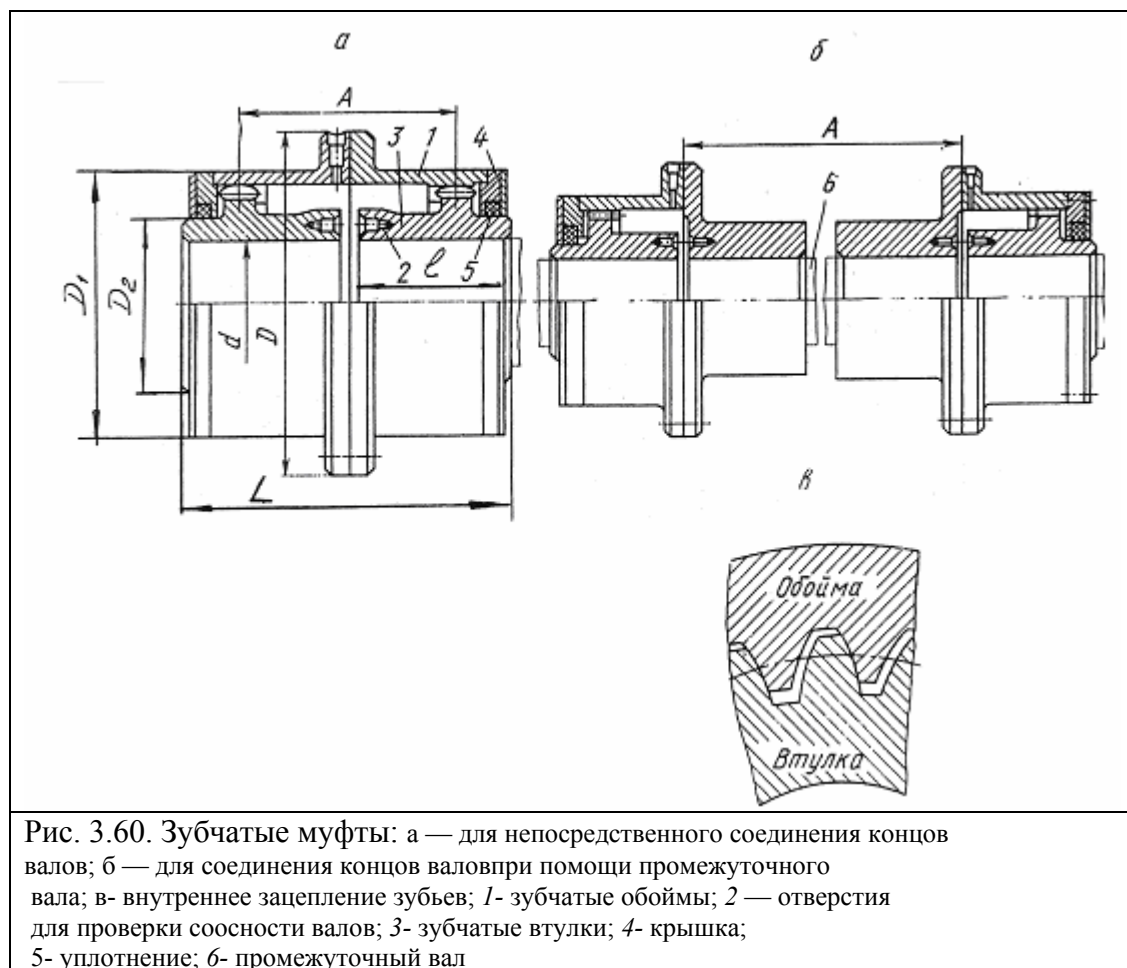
Зубчатые муфты: а — для непосредственного соединения концов валов; б — для соединения концов валов при помощи промежуточного вала; в- внутреннее зацепление зубьев; 1- зубчатые обоймы; 2 — отверстия для проверки соосности валов; 3- зубчатые втулки; 4- крышка; 5- уплотнение; 6- промежуточный вал
